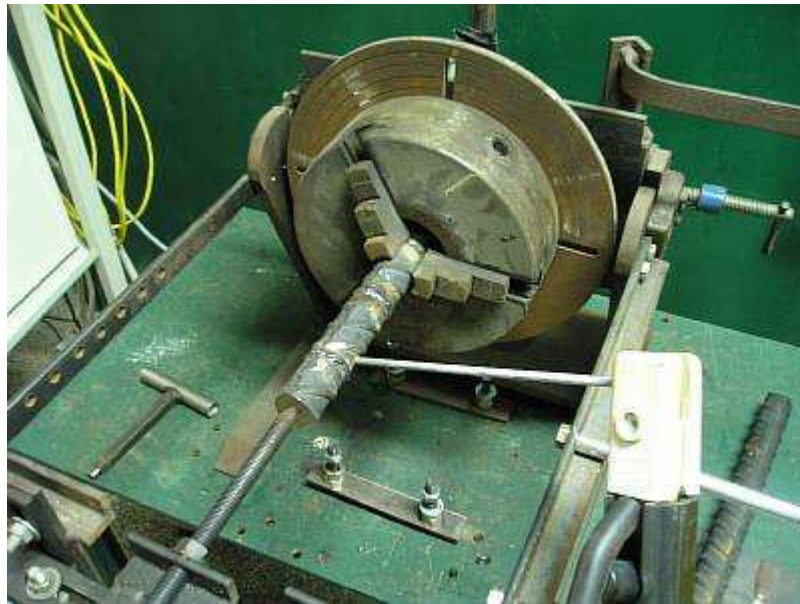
Cabeçote de rotação utilizado na soldagem dos cordões circunferenciais
